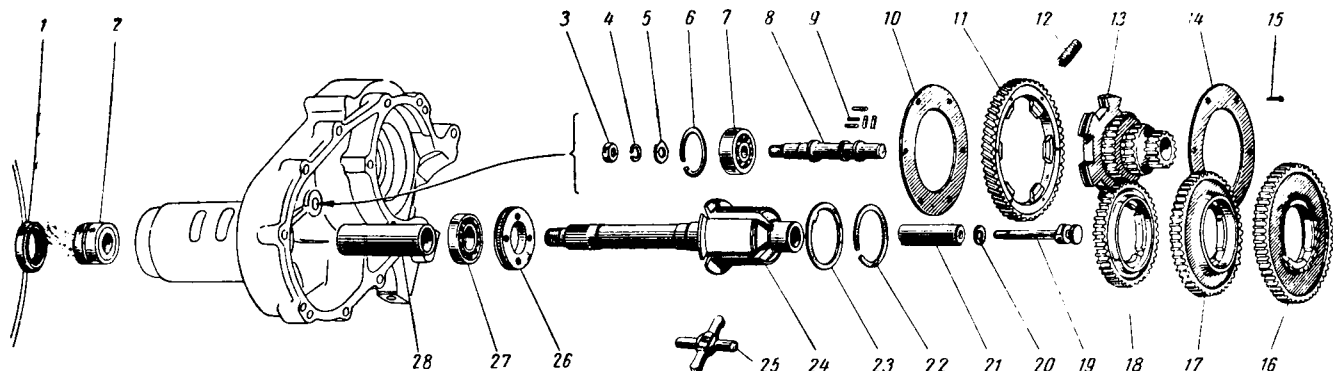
Коробка передач мотороллеров ВП-150 и В-150М:
